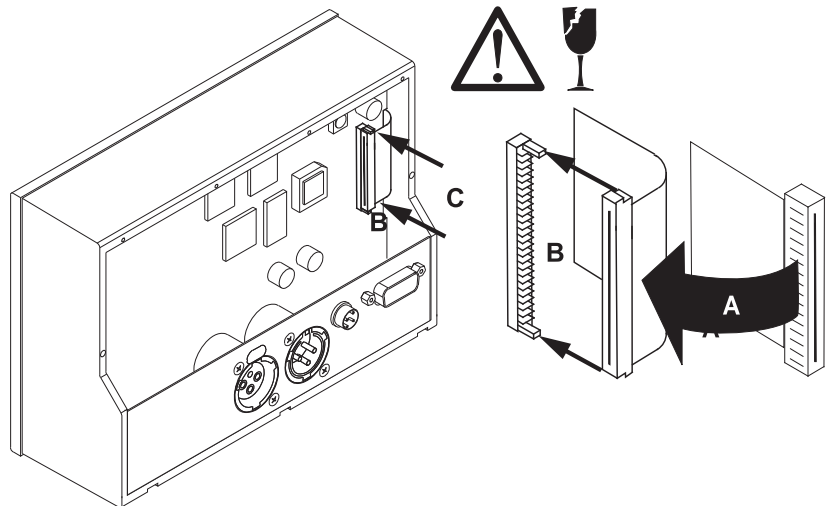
Aufstecken des Flachband-Anschlusskabels auf die Hauptplatine
